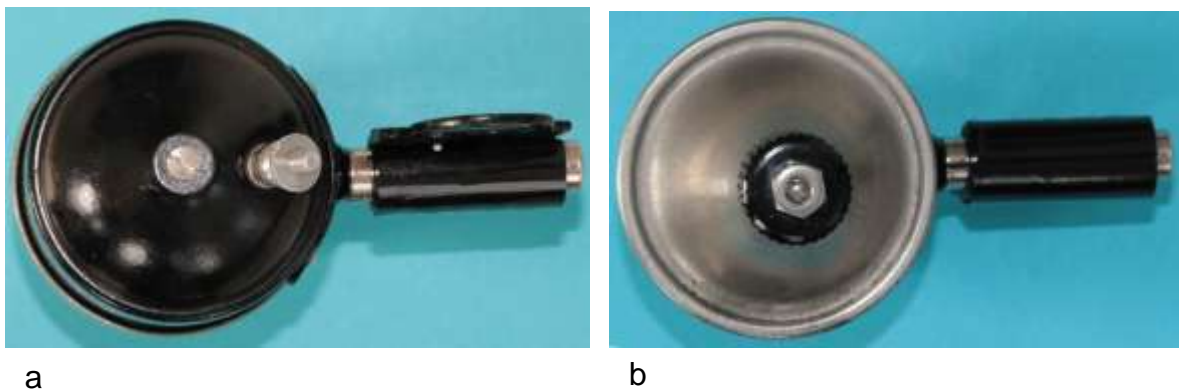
Zwei Ansichten des Gehäuses: a) Boden mit Kabelanschlussbolzen, b) Lagerhals mit Reibrad
